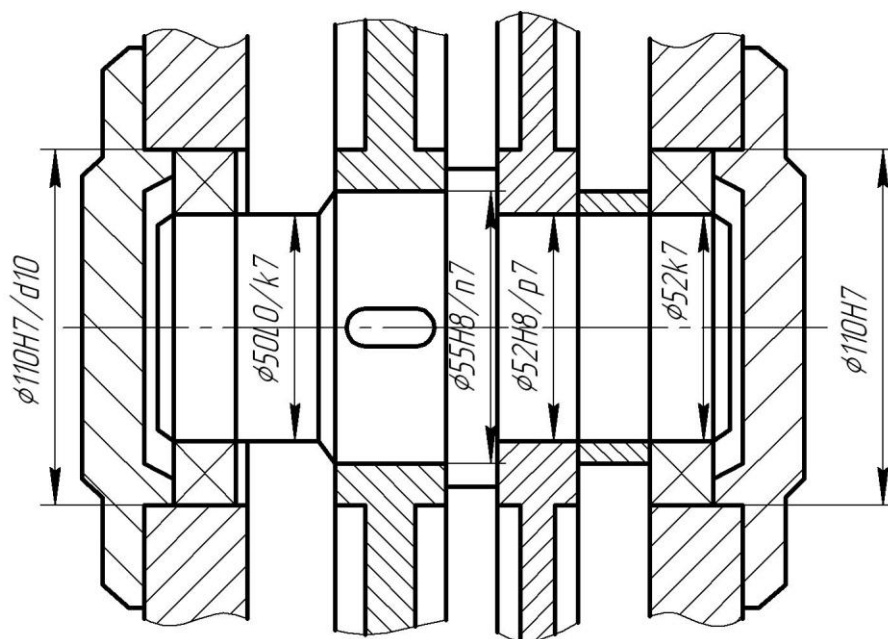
Обозначения посадок подшипника на вал и в отверстие корпуса
